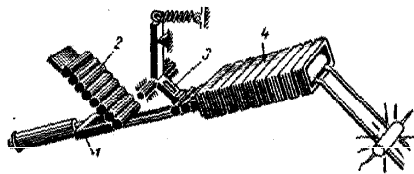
Схема нагревателя для нагрева цилиндрических заготовок в поперечном магнитном поле:
